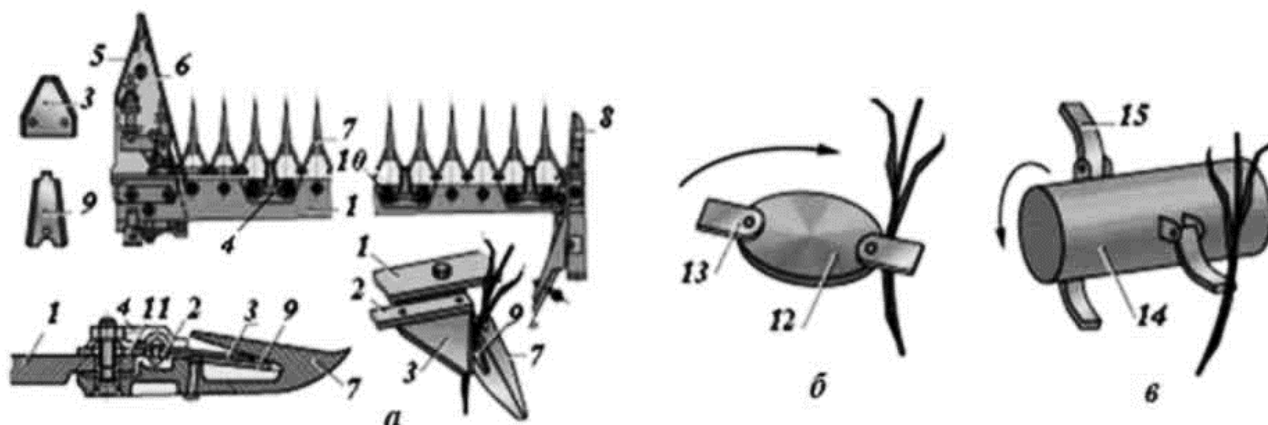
Режущие аппараты косилок: а – сегментно-пальцевый; б – дисковый; в – барабанный; 1 – пальцевый брус; 2 – спинка ножа; 3 – сегмент ножа; 4 – прижим; 5 – внутренний башмак; 6 – отводной пруток; 7 – палец; 8 – внешний башмак; 9 – противорежущая пластина (вкладыш); 10 – резьбовое крепление; 11 – пластина трения; 12 – диск; 13 – нож; 14 – барабан; 15 – нож молотковый
